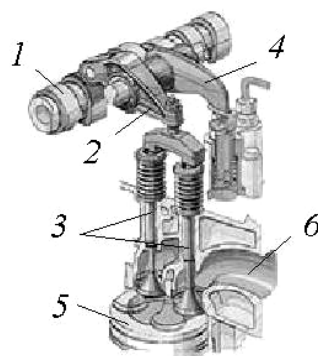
Устройство декомпрессионного моторного тормоза: 1 – газораспределительный вал; 2 – коромысло; 3 – выпускные клапаны; 4 – исполнительный механизм принудительного открытия клапанов; 5 – поршень; 6 – выпускной коллектор
